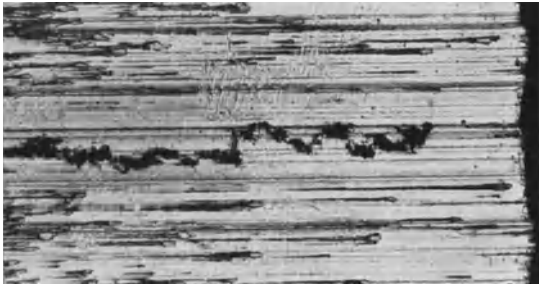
Schlacken in der Schweißnaht eines Kabelmantels.
